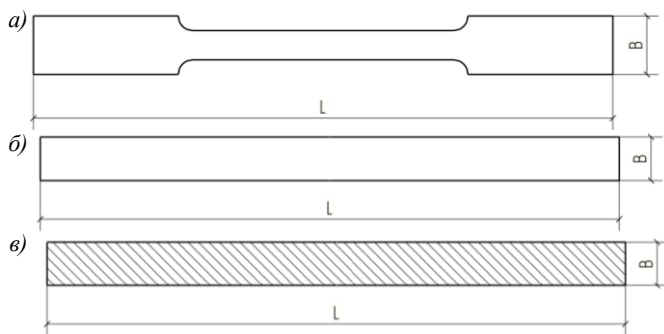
Форма образцов: а – для испытаний на осевое растяжение; б – для испытаний на изгиб; в – композитных деталей
